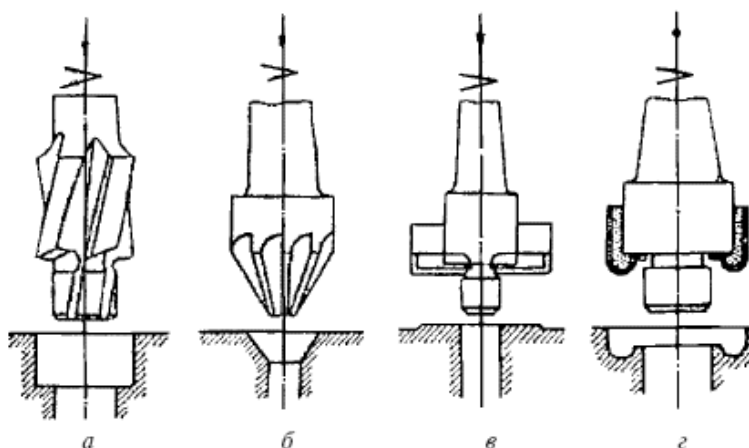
Зенкеры: а – цилиндрические для зенкерования сквозных или глубоких отверстий; б – конические для снятия фасок и образования конических углублений; в – торцевые для зенкерования торцевых поверхностей приливов (торцовки); г – фасонные для зенкерования фасонных поверхностей
